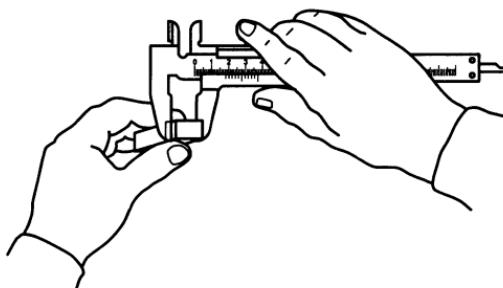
Использование штангенциркуля для измерения наружного размера детали
